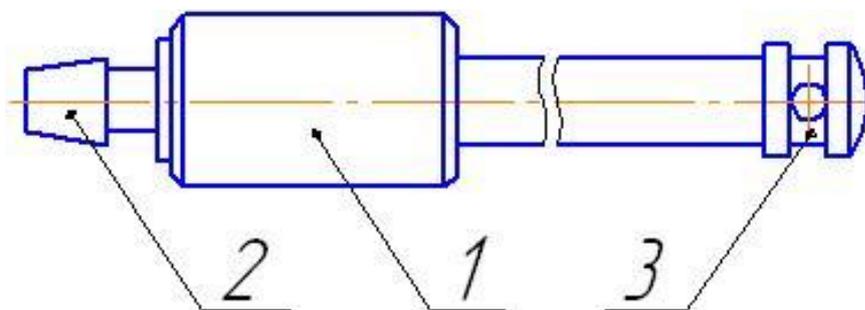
Внешний вид зонда воздухозаборного: 1- корпус, 2-штуцер, 3 – наконечник.
